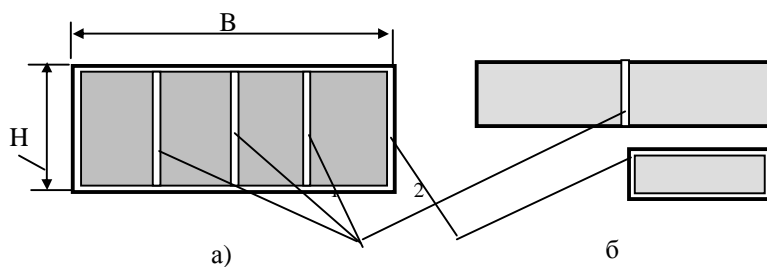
Схемы получения чистовых заготовок (дялянок) из черновых заготовок для толстых (а) и тонких (б) досок: 1 - пропилы; 2 - припуски на фрезерование.
